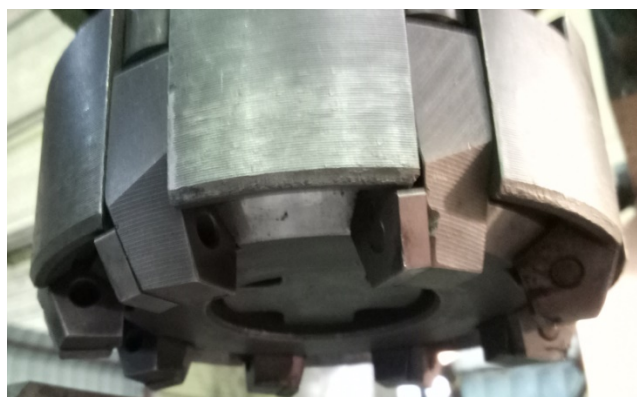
Скоростная фрезерная головка с пятигранными режущими пластинами
